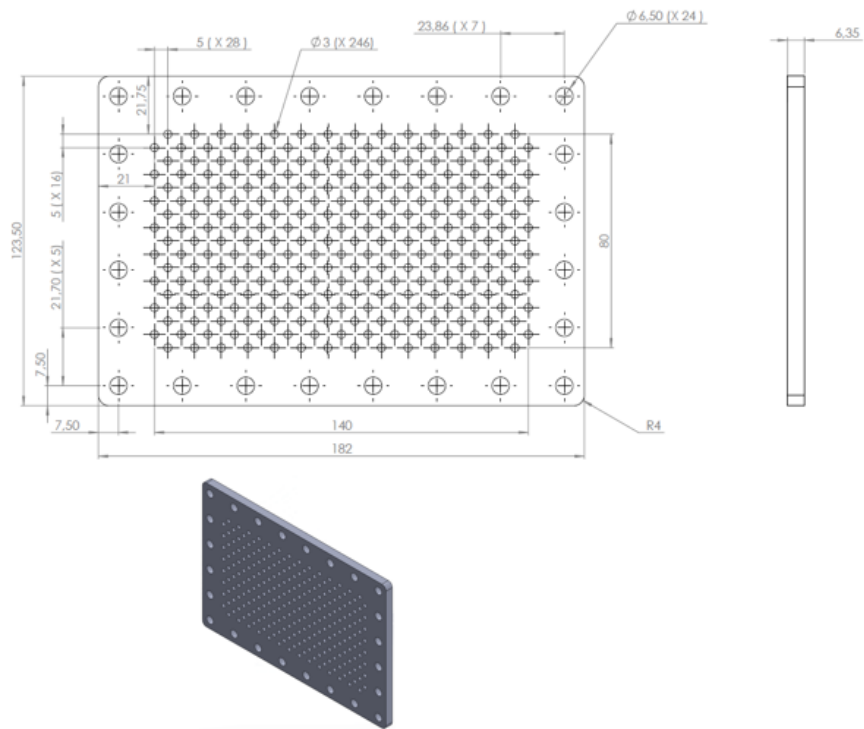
Desenho técnico da segunda placa furada do retificador.
